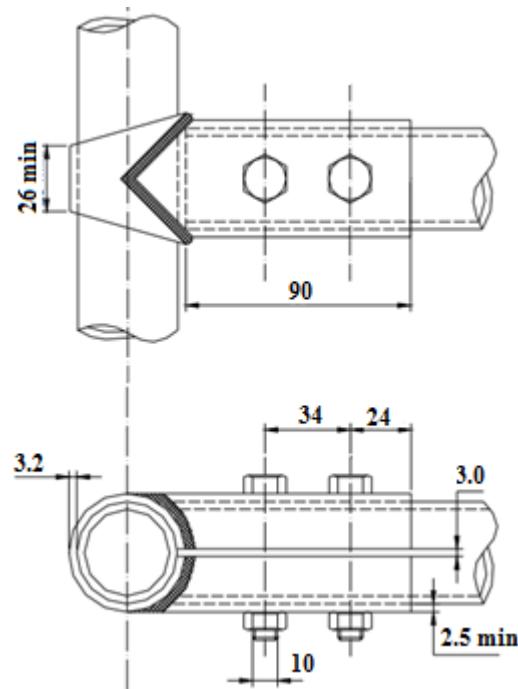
Conexión desmontable con acople soldado.
